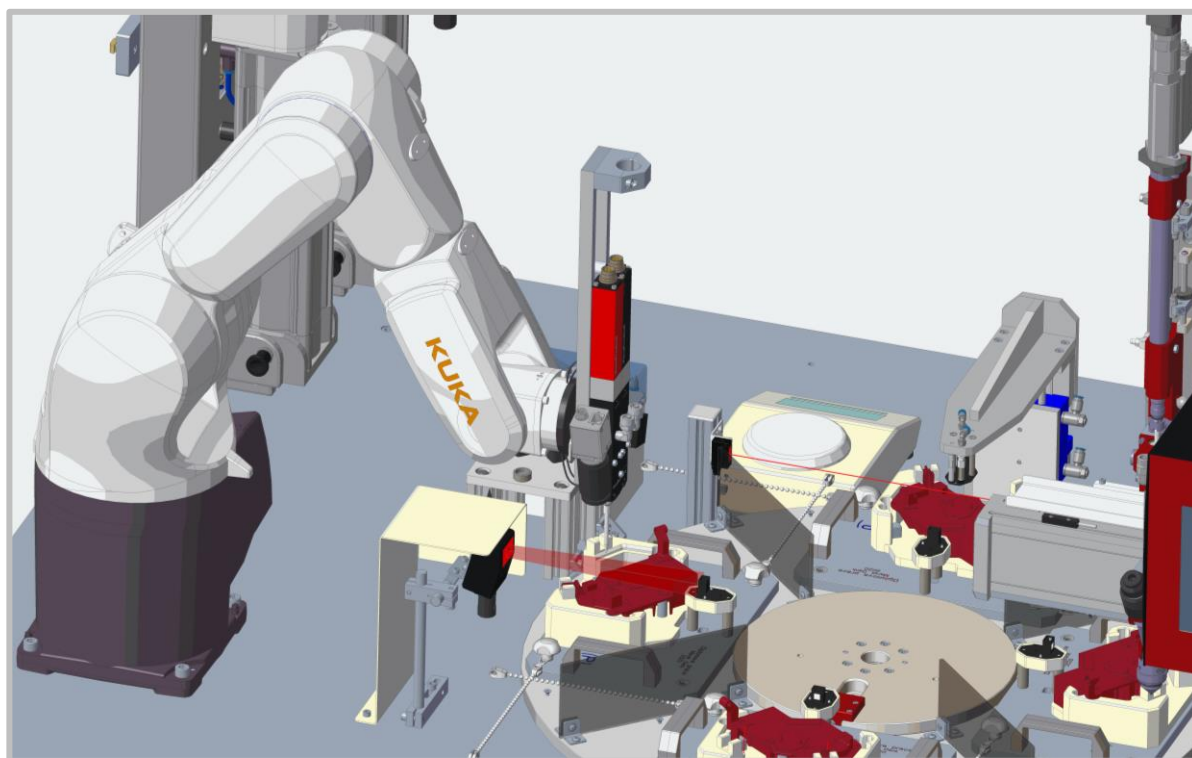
Pohled do pracovního prostoru operátora ve fázi, kdy je založena DPS, chladič však nikoliv. Šablona šroubování se nachází v horní pozici a blokovací mechanismu s podpíracím mechanismem jsou v zasunuté poloze. Nad lůžkem jsou zřetelně viditelné tři optické paprsky snímačů BOS01WT, BOS01WW a BOS01JP.
